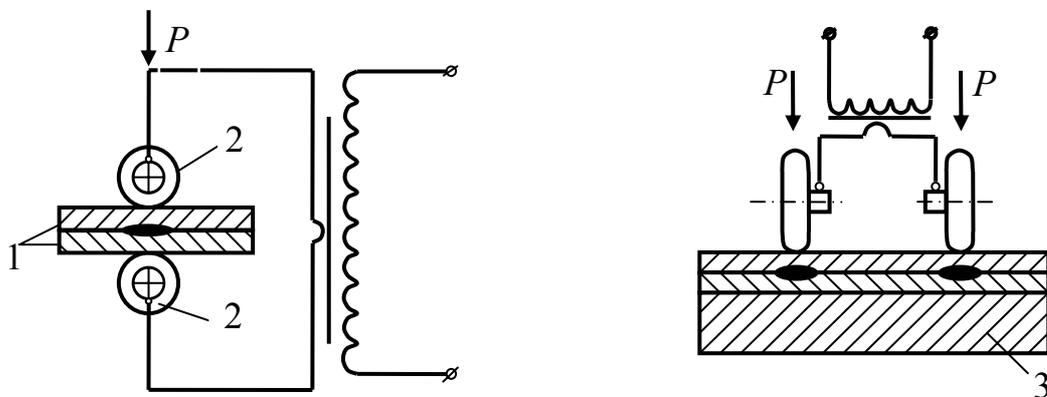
Принципиальная схема шовной сварки:
